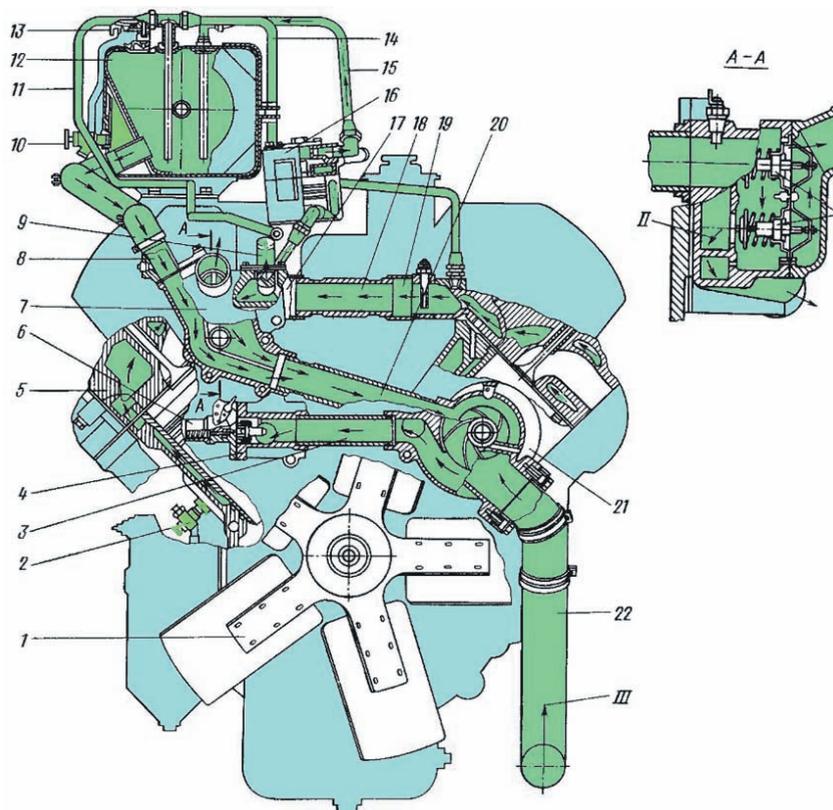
Схема системы охлаждения: 1 — вентилятор; 2 — сливной кран системы охлаждения; 3 — труба подводящая правого полублока; 4 — патрубок подводящей трубы; 5 — головка цилиндров; 6 — выключатель гидромолота привода вентилятора; 7 — трубка соединительная от компрессора к бачку; 8 — трубка соединительная от компрессора к бачку; 9 — трубка соединительная от компрессора к бачку; 10 — кран контроля уровня охлаждающей жидкости; 11 — труба воздухоотводящая от радиатора; 12 — бачок расширительный; 13 — пробка паровоздушная; 14 — трубка перепускная от двигателя к расширительному бачку; 15 — трубка соединительная от компрессора к бачку; 16 — компрессор; 17 — труба водосборная правая; 18 — труба соединительная; 19 — труба водосборная левая; 20 — трубка перепускная термостатов; 21 — насос водяной; 22 — колено отводящее патрубка водяного трубопровода; 23 — термостат; I — в радиатор при открытых термостатах; II — в насос при закрытых термостатах; III — из радиатора.
